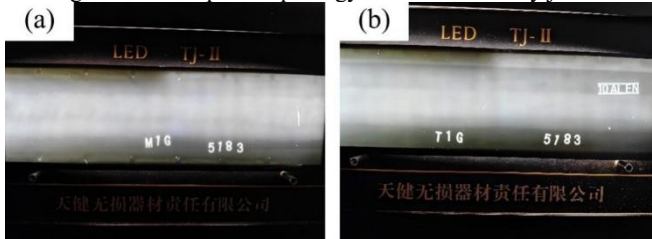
铝合金焊接接头 X 射线探伤结果(a)MIG 焊接(b)TIG 焊接
